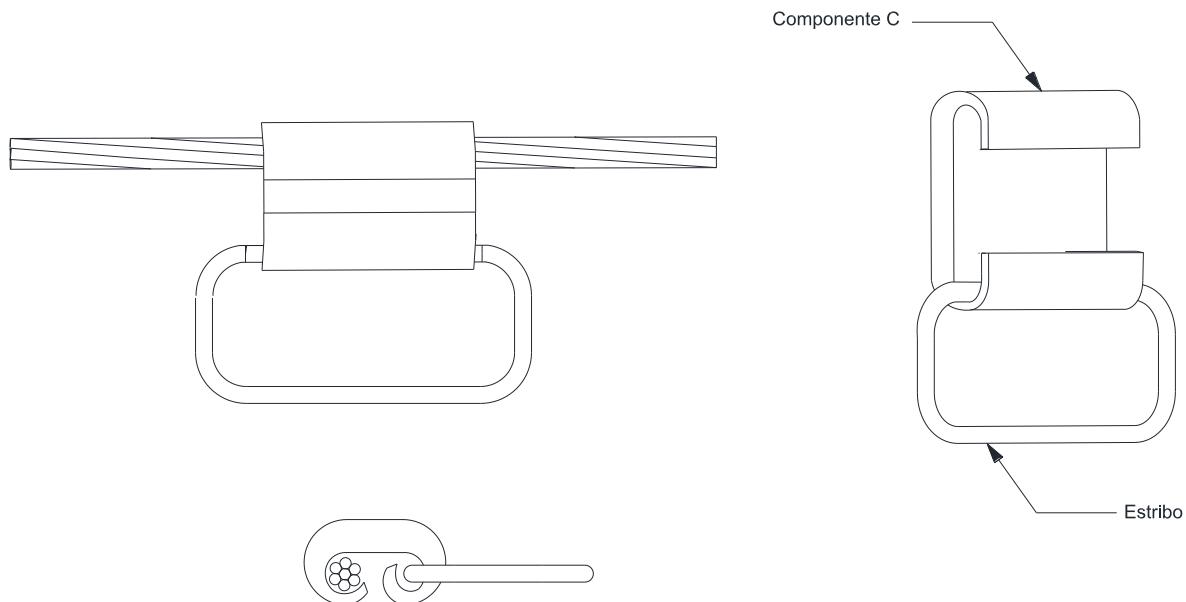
Conexões – Conector de compressão tipo “C” com estribo
